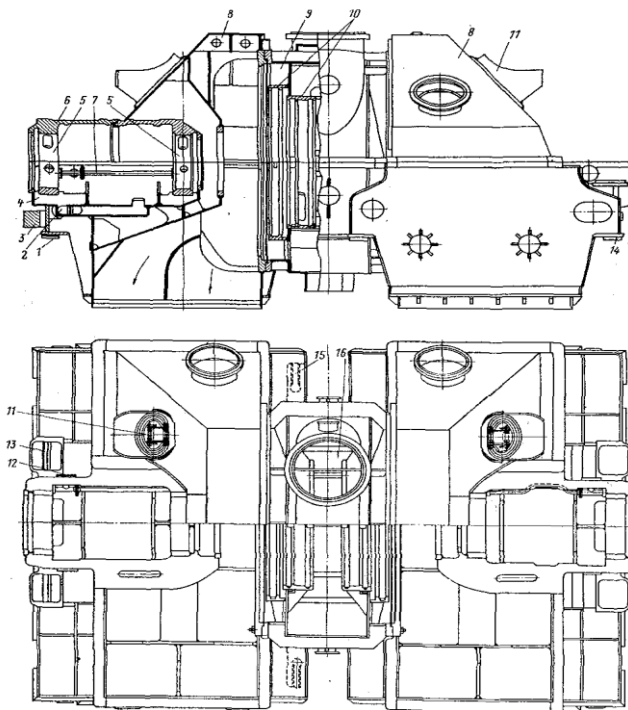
Конструкція одностінного корпуса ЦНТ
